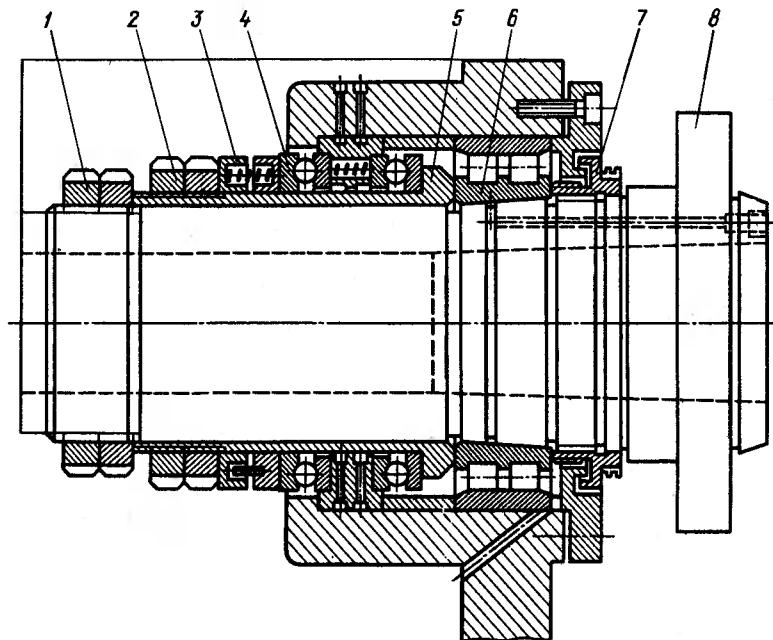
Передняя опора шпинделя токарного станка на подшипниках качения
